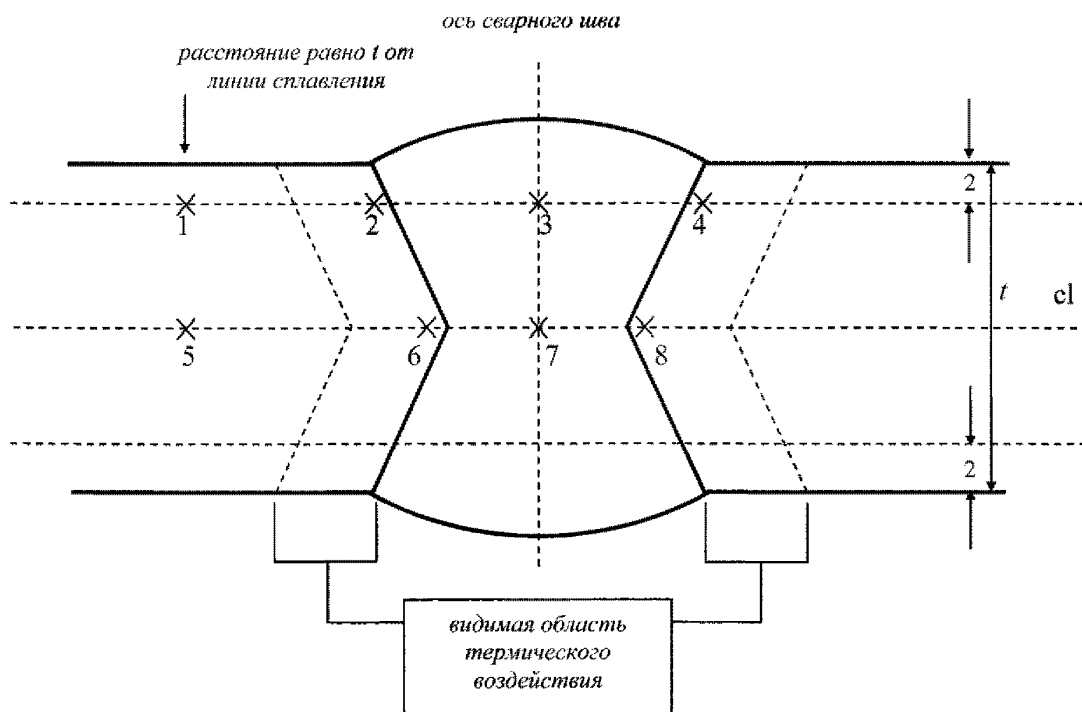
Испытание твердости продольного сварного шва.
